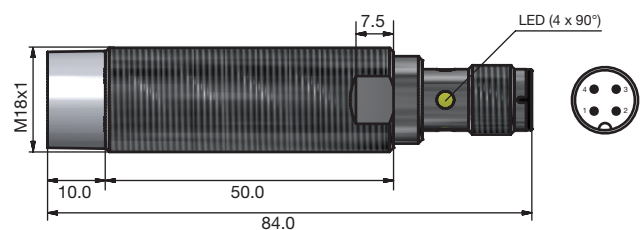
Lange Ausführung, Nicht bündiger Einbau, Steckversion
